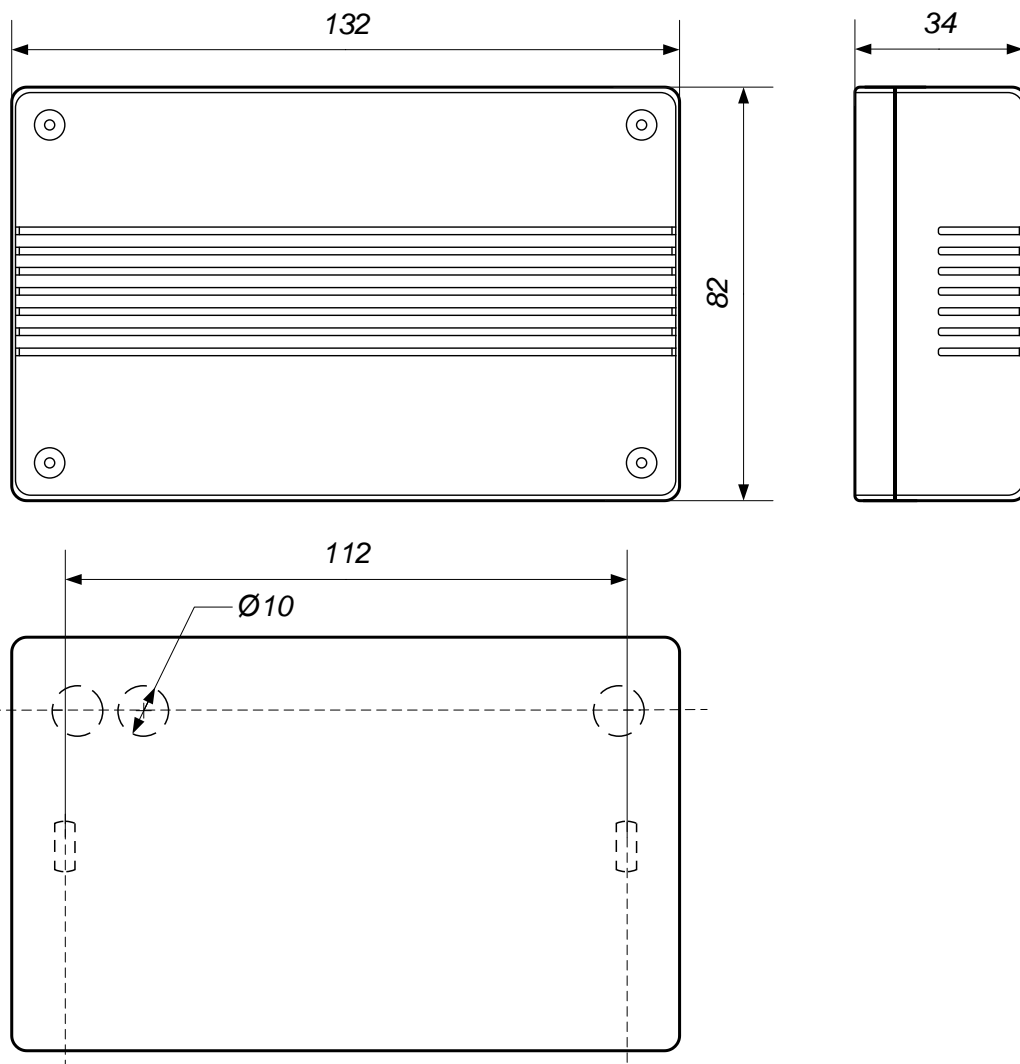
Габаритные размеры изделия в корпусе 115
